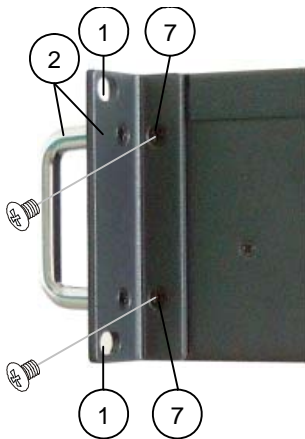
19" Winkel mit Griff und Befestigungsschrauben
